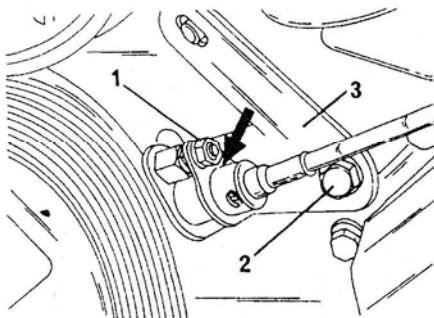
Крепление датчика верхней мертвой точки на крышке распределительного механизма (четырёхцилиндровый двигатель).
